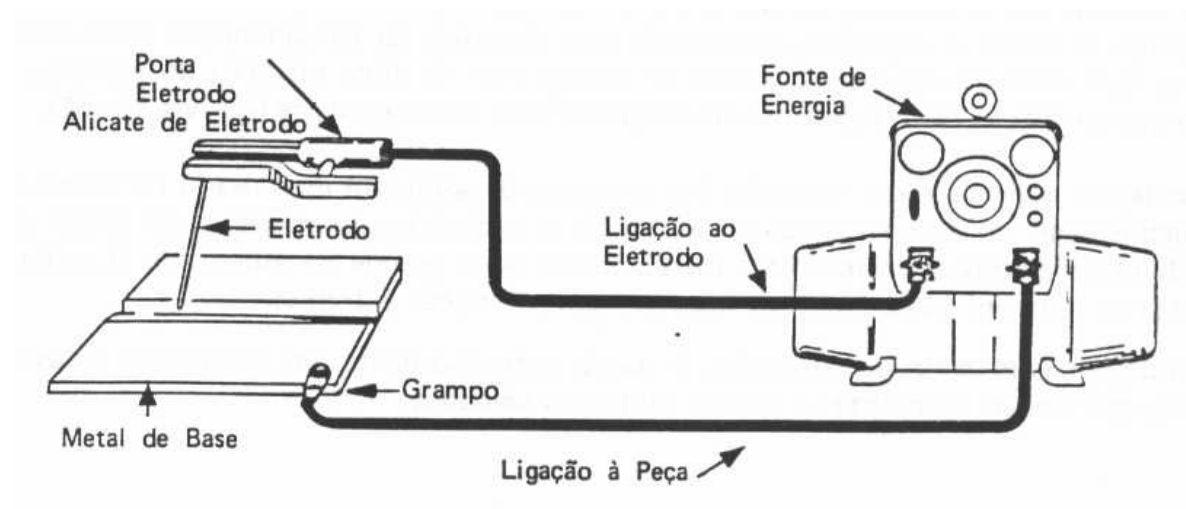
Equipamento para soldagem com eletrodo revestido
